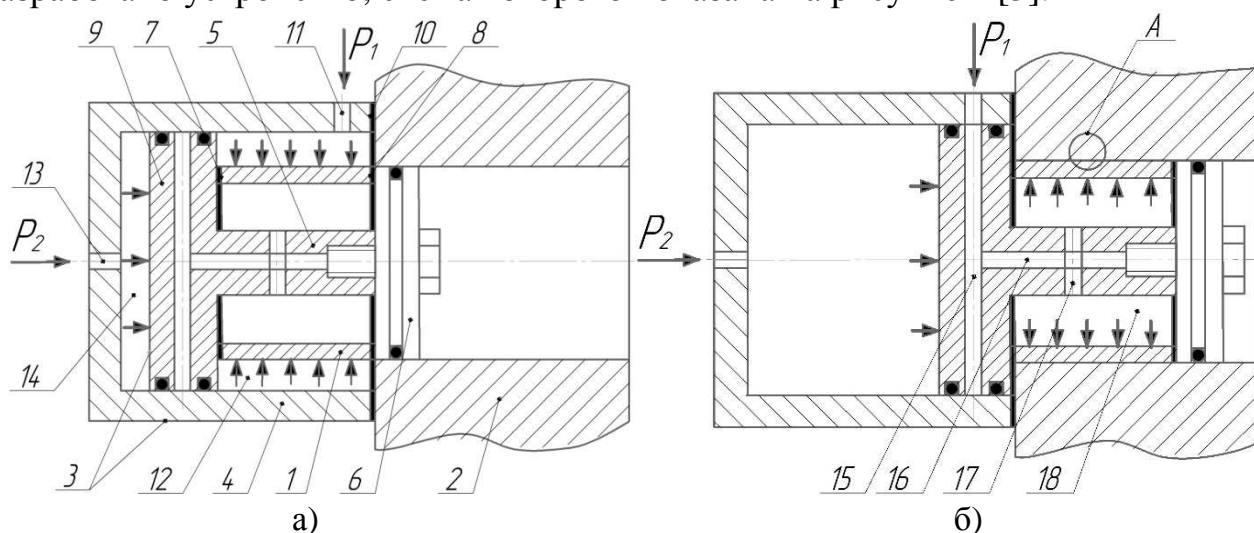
Схема устройства для запрессовки цилиндрической втулки в отверстие корпусной детали: а, б – начальное и конечное положения устройства:
